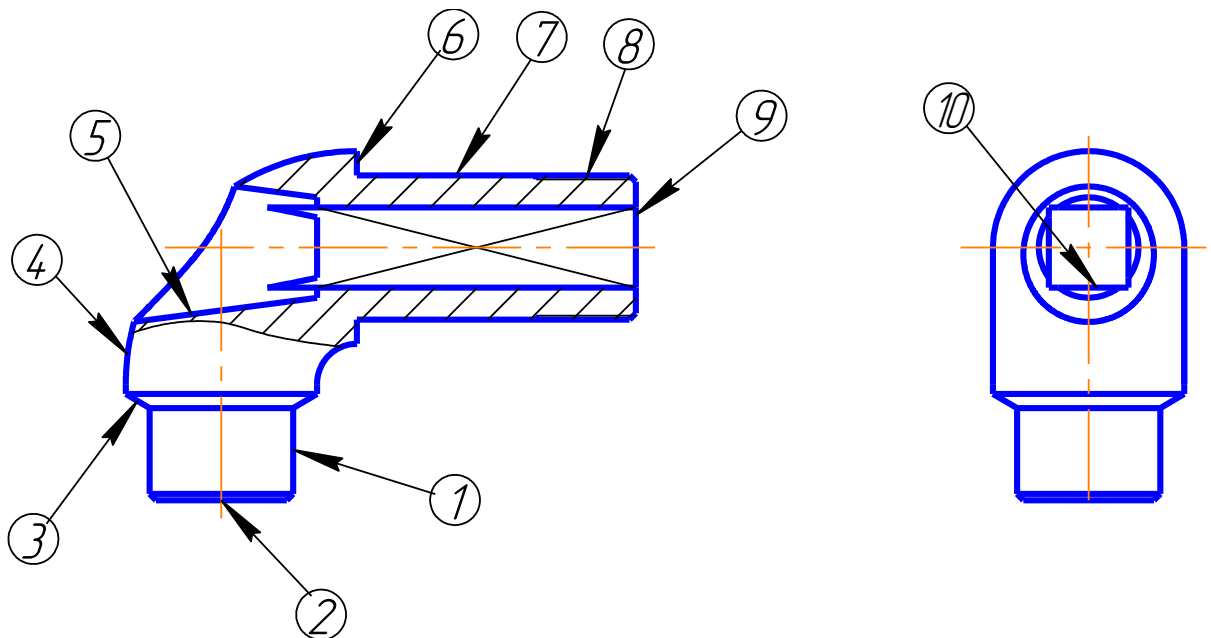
Конструкція и основні робочі поверхні деталі «Цапфа важеля»
